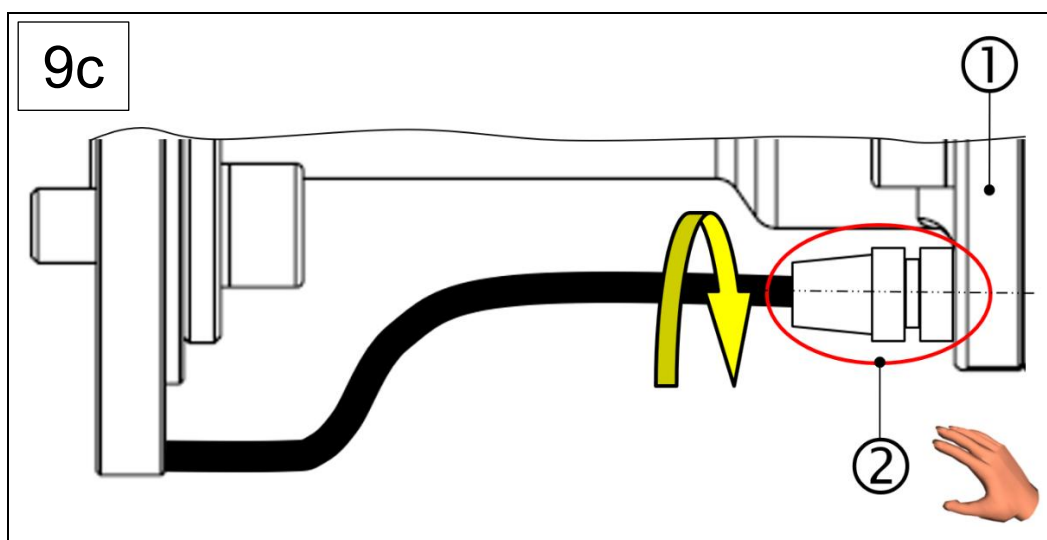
Montaggio dell'unità sensore, BEAROMOS® 2020 (variante corta, passaggi 1-9)
